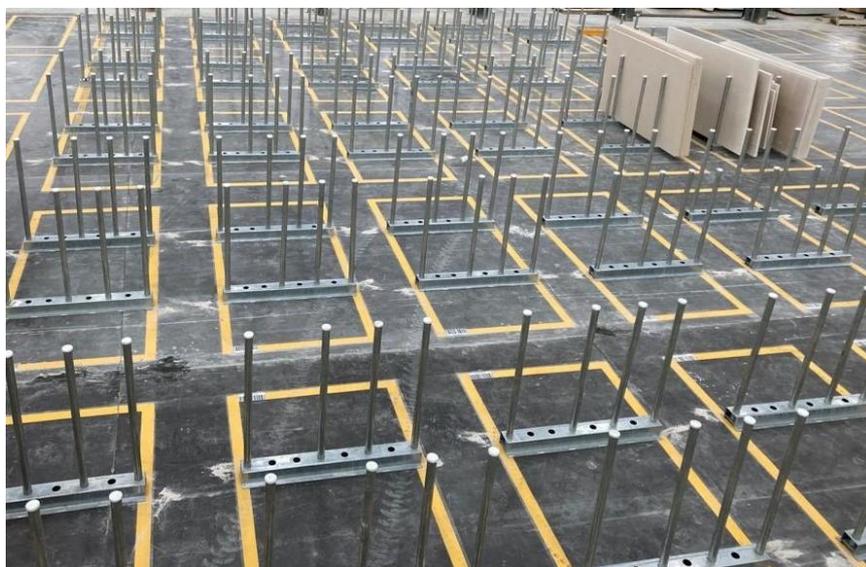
Stock de chapa CTA-1 que já sofreu o processo de inspeção na linha de *trimming
